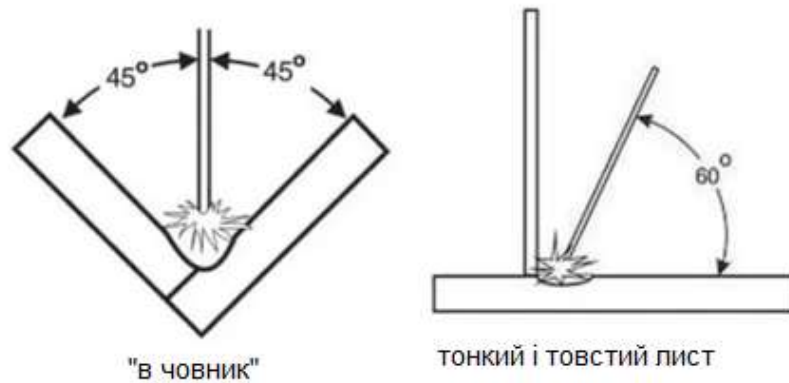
Зварювання шва «в човник» та при з'єднанні металів різної товщини
